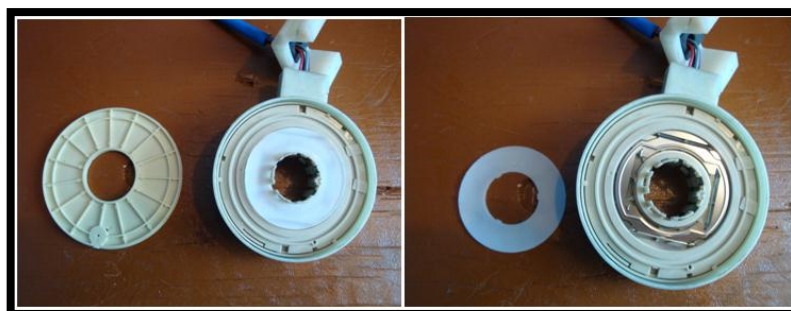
Desmontaje de la tapa y rodela del sensor de par
